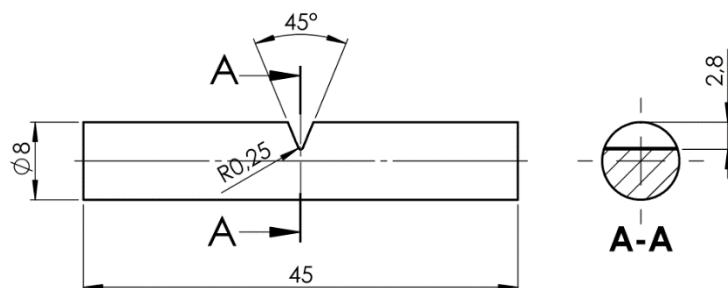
Eprouvettes rondes avec entaille en V, dimensions en mm
